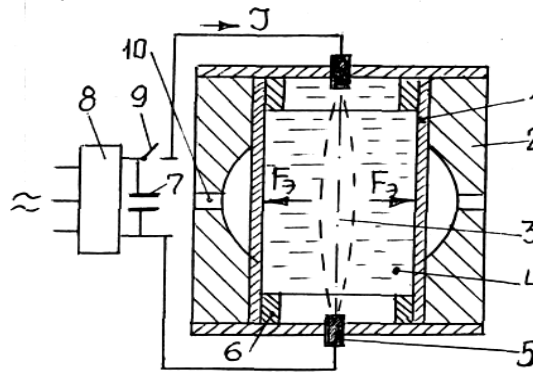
Схема електрогідравлічної обробки: 1 – заготовка; 2 – матриця; 3 – речовина; 4 – рідина; 5 – електроди; 6 – ущільнювальні деталі; 7 – конденсаторна батарея; 8 – випростувач; 9 – перемикач; 10 – отвір для видалення повітря
